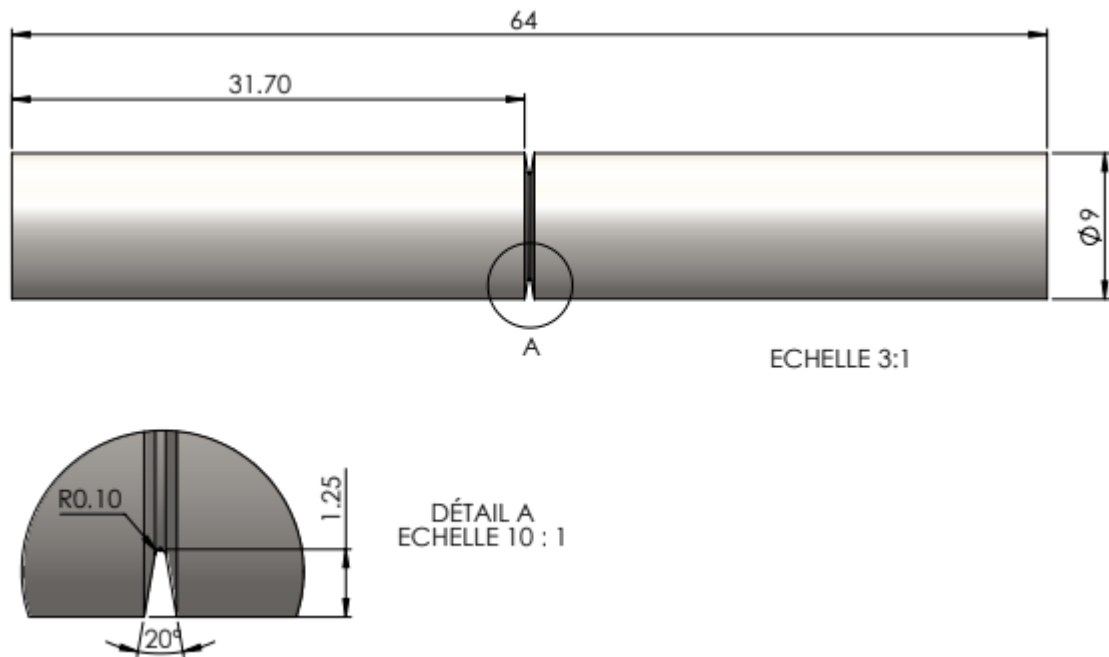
Géométrie et dimension de l'éprouvette V20R0.1
